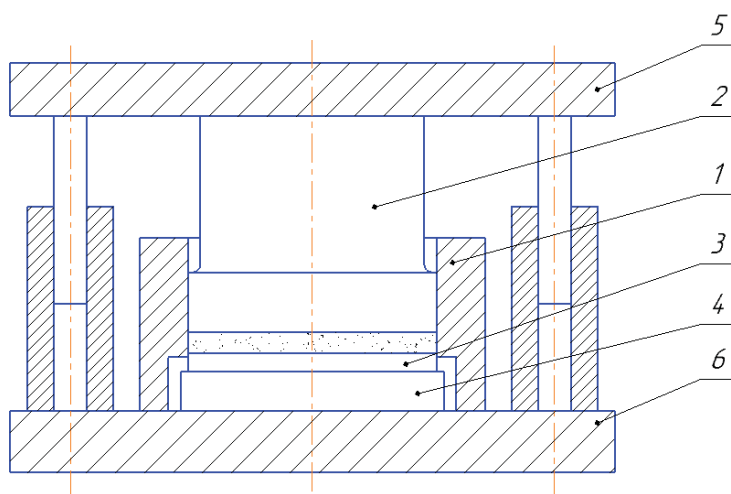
Пресс-форма для доуплотнения пластины с ее калибровкой
